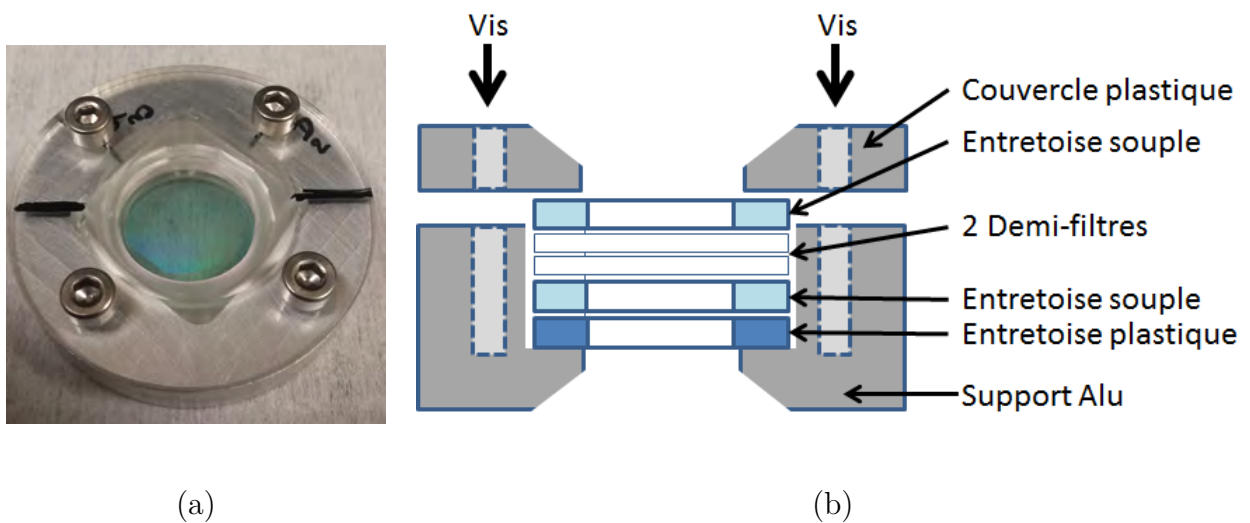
Porte-filtre : (a) vue du filtre assemblé dans son support , (b) schéma en coupe de l'assemblage du filtre et du support.
